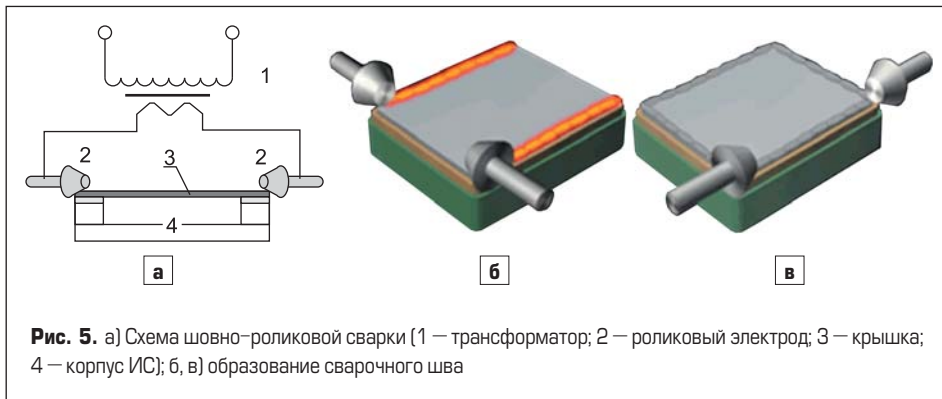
а) Схема шовно-роликовой сварки (1 — трансформатор; 2 — роликовый электрод; 3 — крышка; 4 — корпус ИС); б, в) образование сварочного шва
